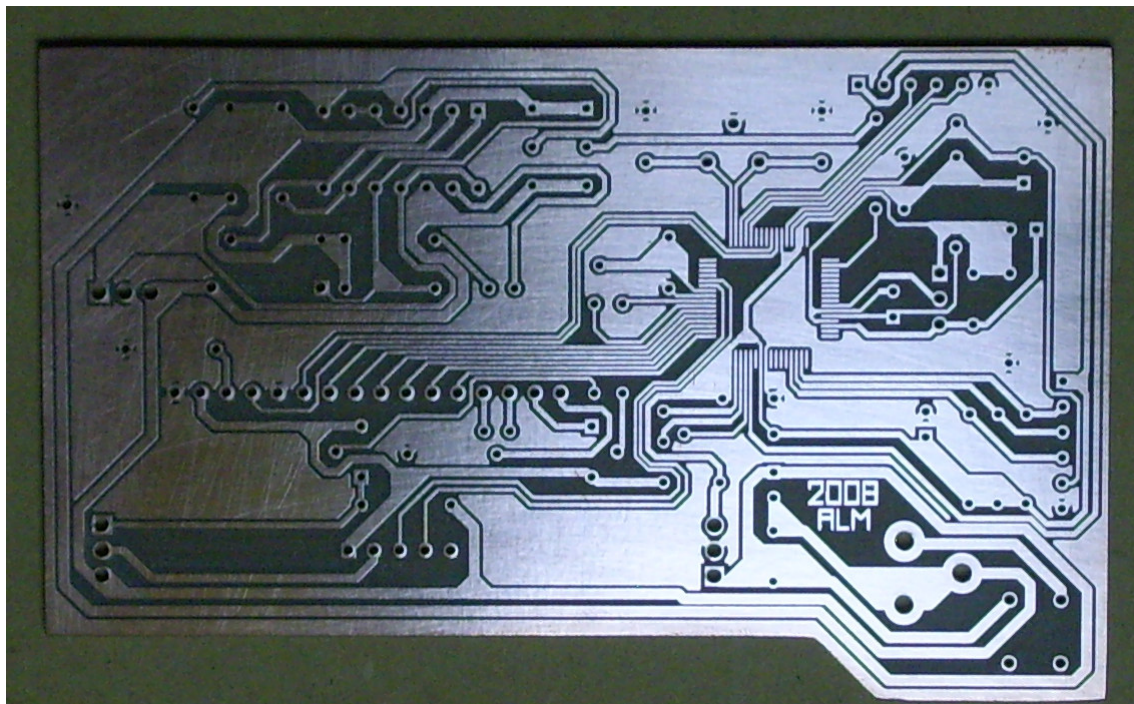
Face inferior da placa de circuito impresso do Módulo Móvel
